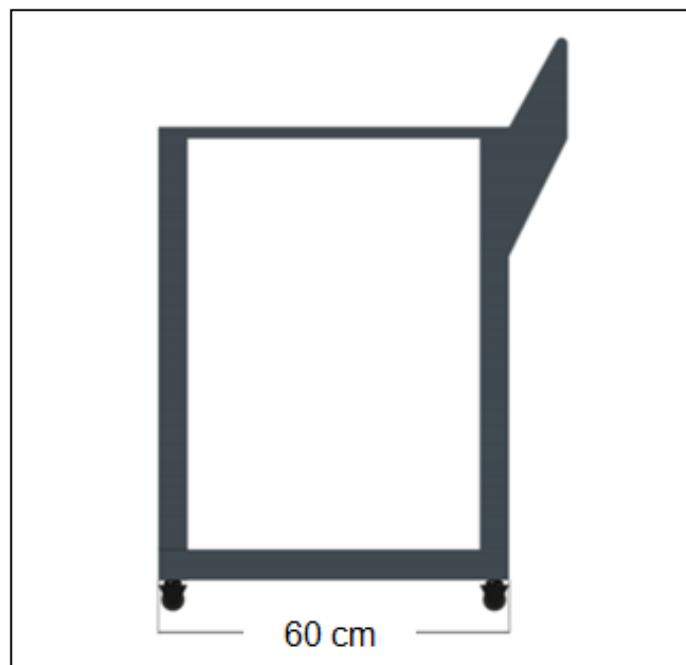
Dimensiones de la Estructura 2 - Vista lateral
